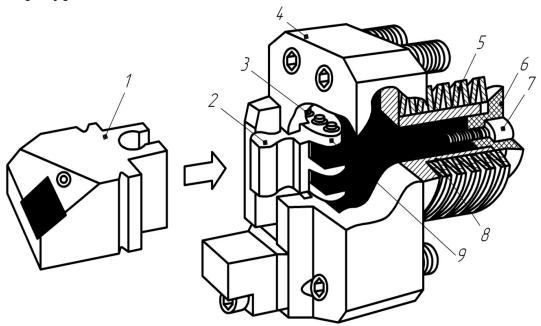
Схема вспомогательного блока для крепления модульного режущего инструмента
